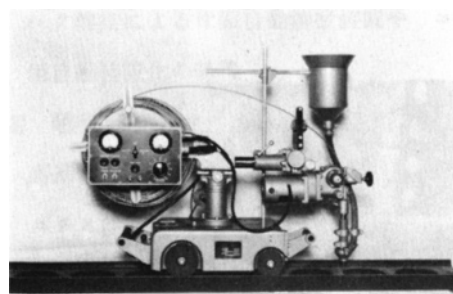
初期のサブマージアーク溶接機 (造船の溶接—35年の歩み)
